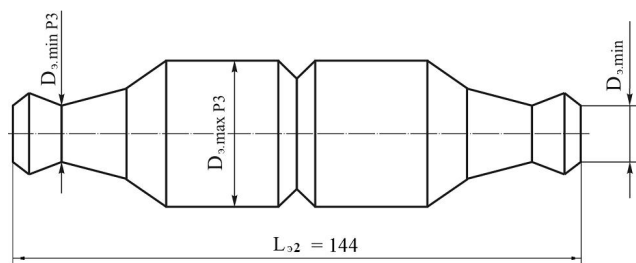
Эскиз формы развертки расчетной заготовки для спаренной штамповки двух поковок «рым-болт»
